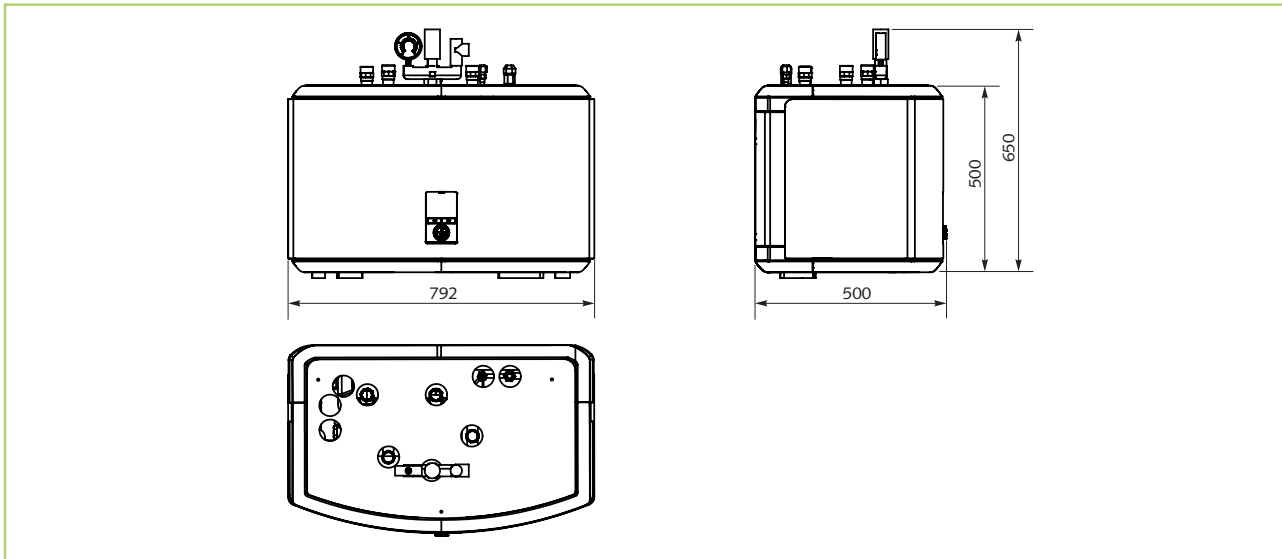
Abmessungen Innenmodule Serie WKF 85/120/180
